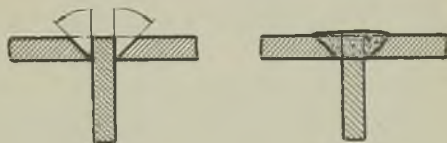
Herstellung eines T-Eisens: a) Vorbereitung (Abschrägen und Zusammenpassen der Nähte); b) Schweißung.
